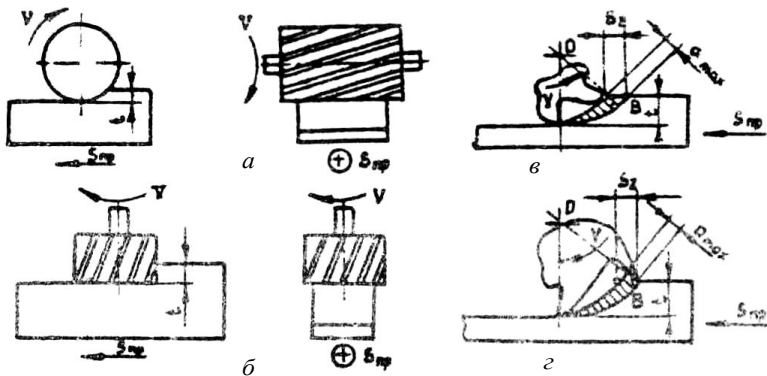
Схемы фрезерования: цилиндрической (*а*) и торцевой (*б*) фрезами: встречного (*в*) и попутного (*з*): 1 – заготовка, 2 – фреза
